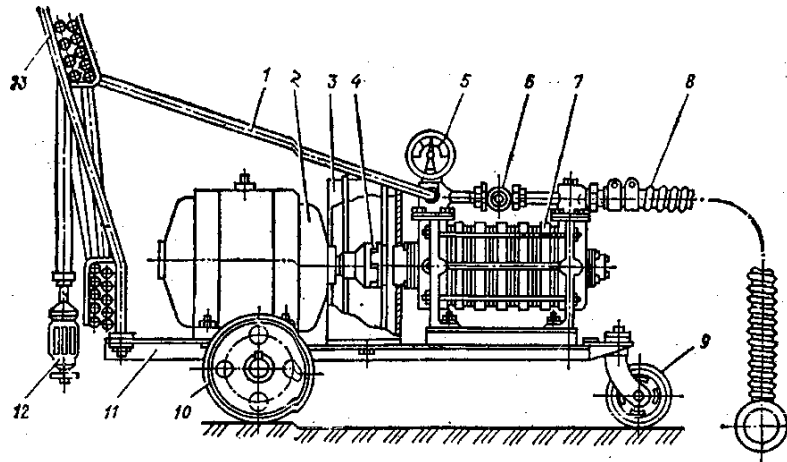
Мийна установка 5BCM-1500: 1 — напірний рукаву 2 — електродвигун; 3 — кожух; 4 — з'єднувальна муфта, перепускний клапан - 5 — насос; 6 — кран; 7 — барабан; 8 —забірний рукав; 9, 10 — Колеса; 11 — рама; 12 — мийний пістолет; 13 — рукоятка
